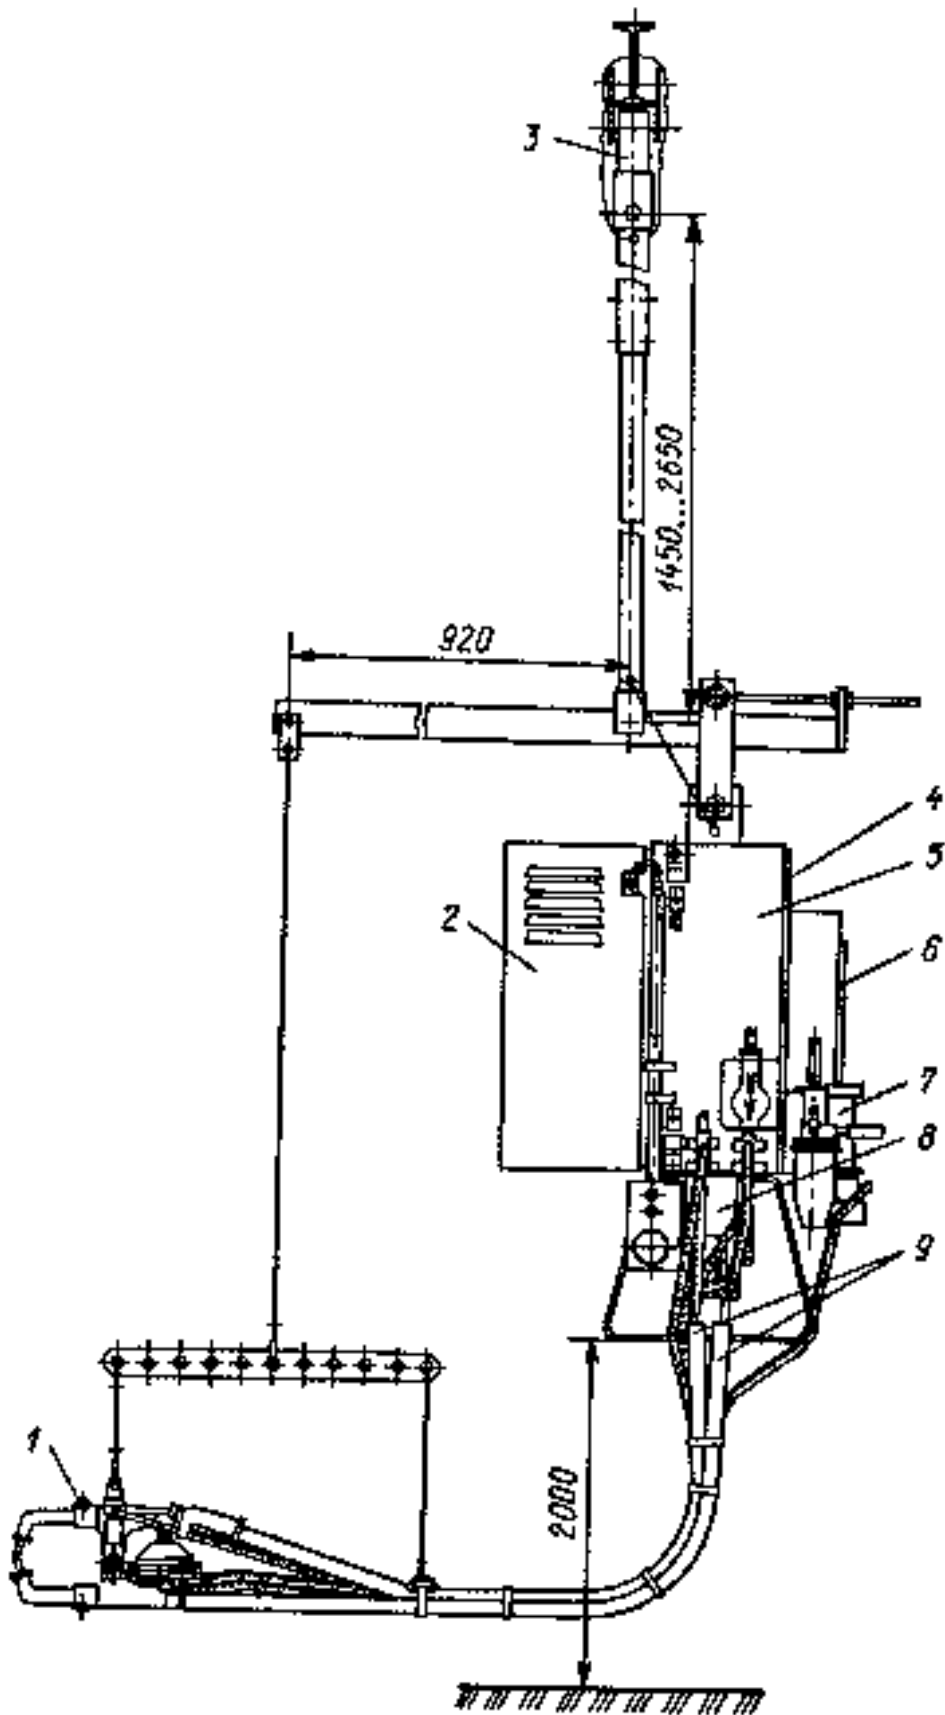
Машина сварочная типа МТП-1110
